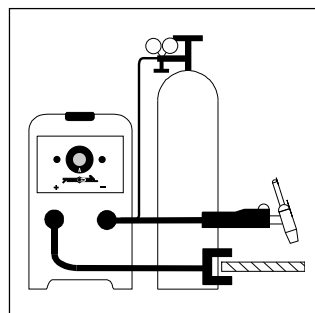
TP 1400 ausgerüstet zum WIG-Schweißen
